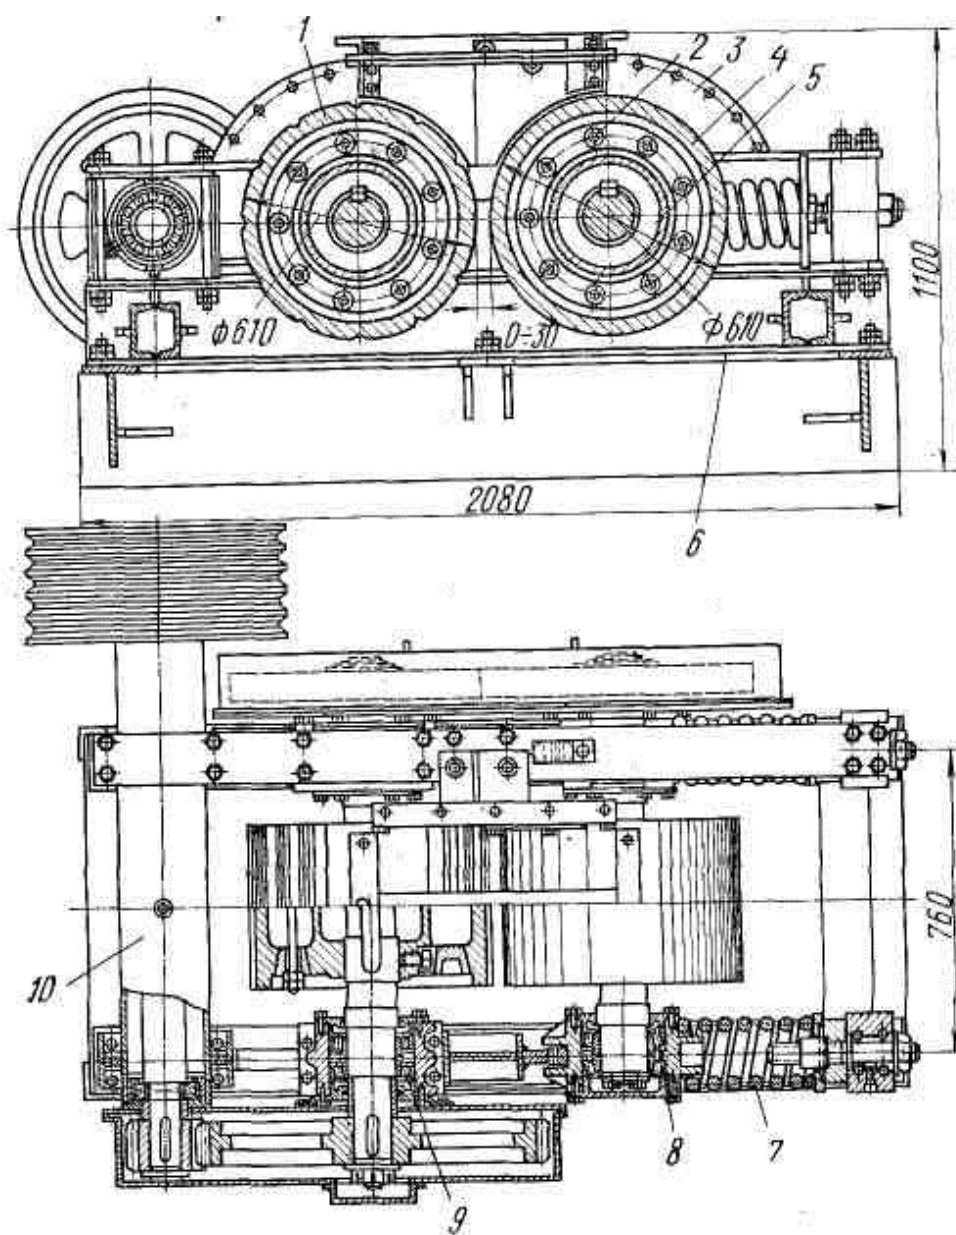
Двухвалковая дробилка СМ-12Б
